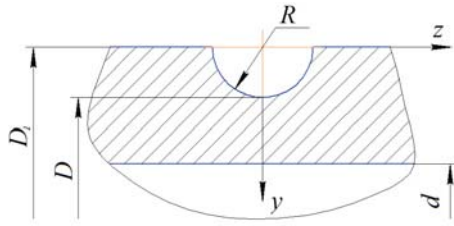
Цилиндрический образец с надрезом полукруглого профиля
